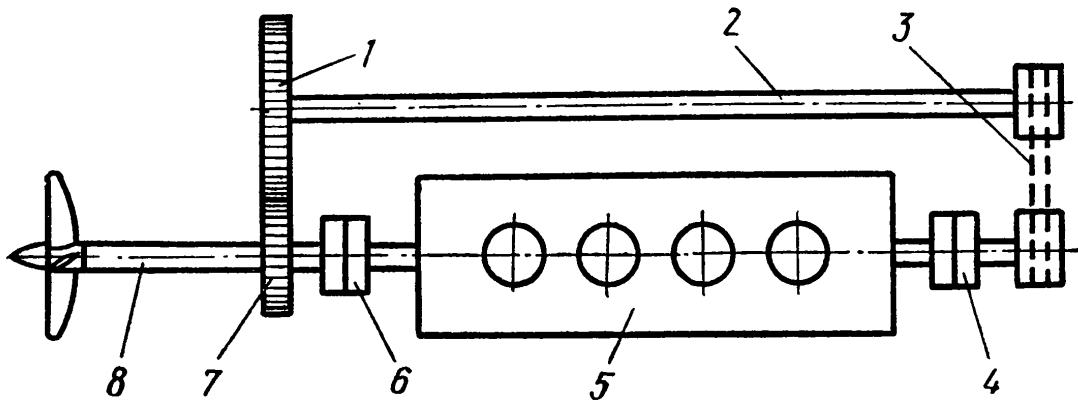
Схема системы реверса дизеля конструкции инженера Р. А. Корейво:
